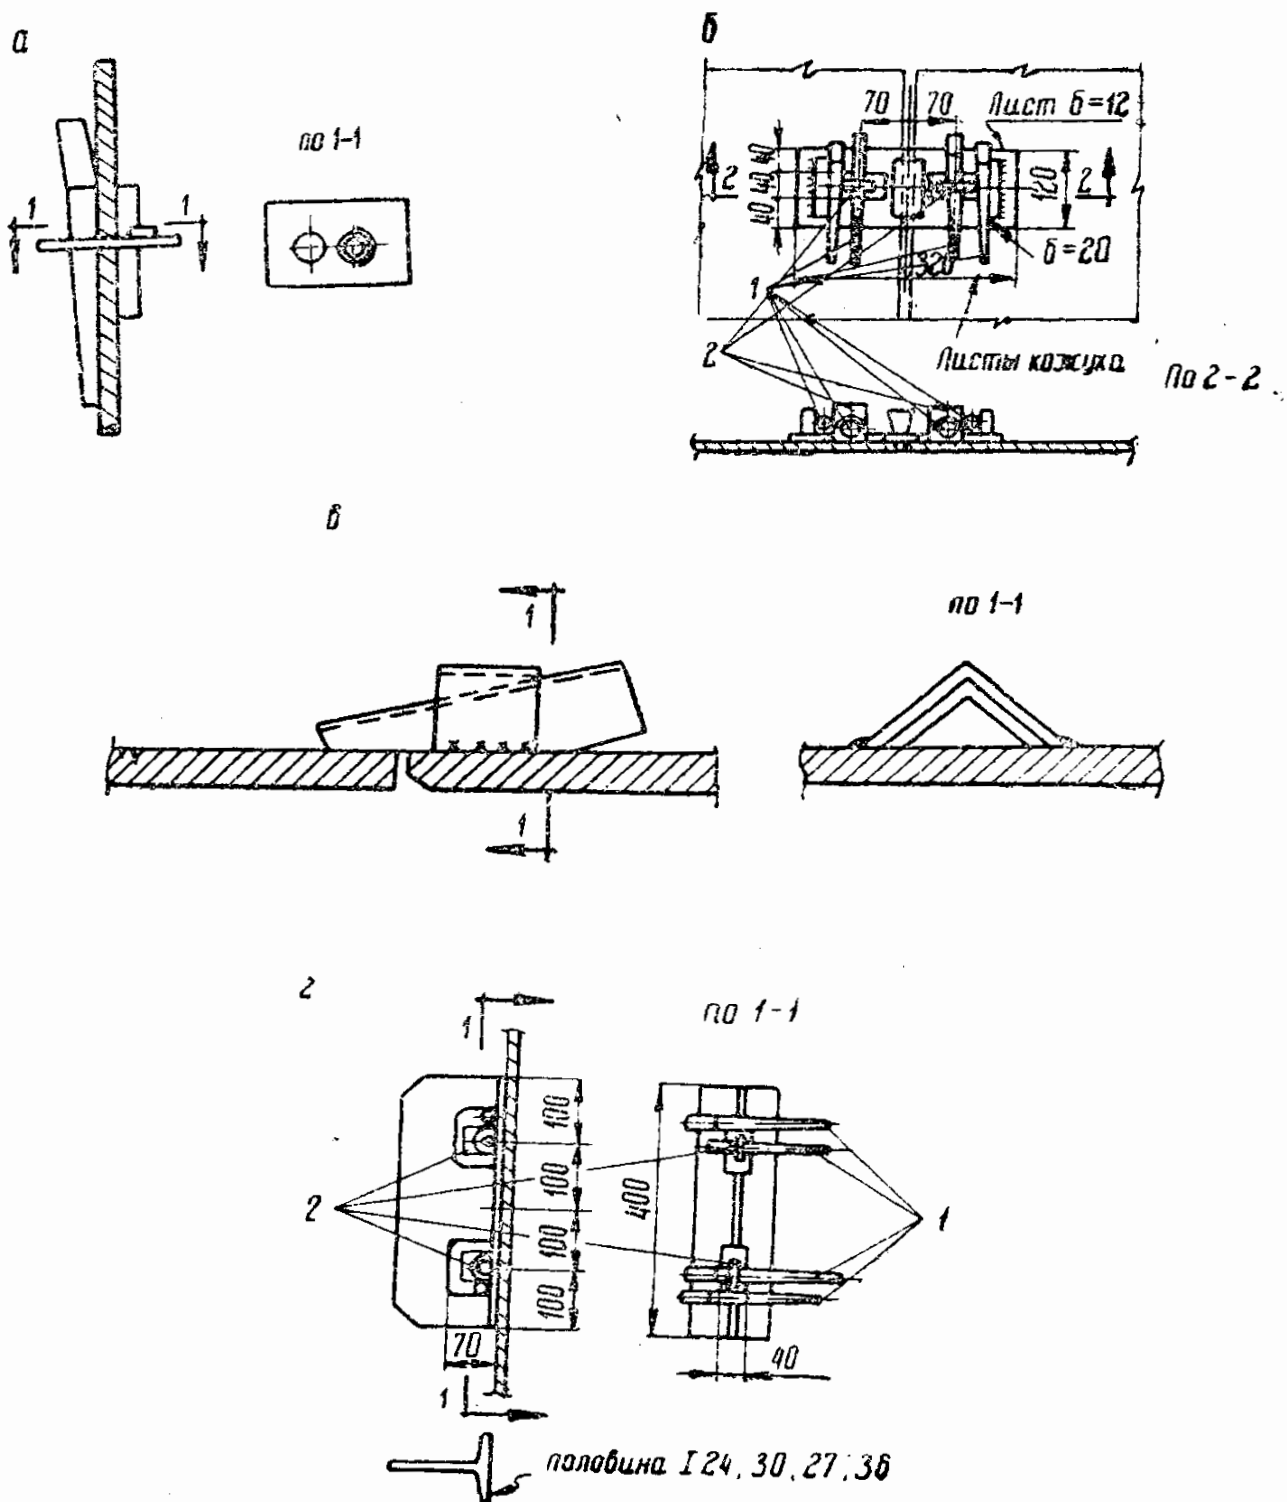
Инвентарные приспособления для сборки листовых конструкций. а — прокладка с оправками; б — стяжная планка; в — уголок, обрезанный на клин; г — стяжной тавр; 1 — клинья; 2 — шайбы
